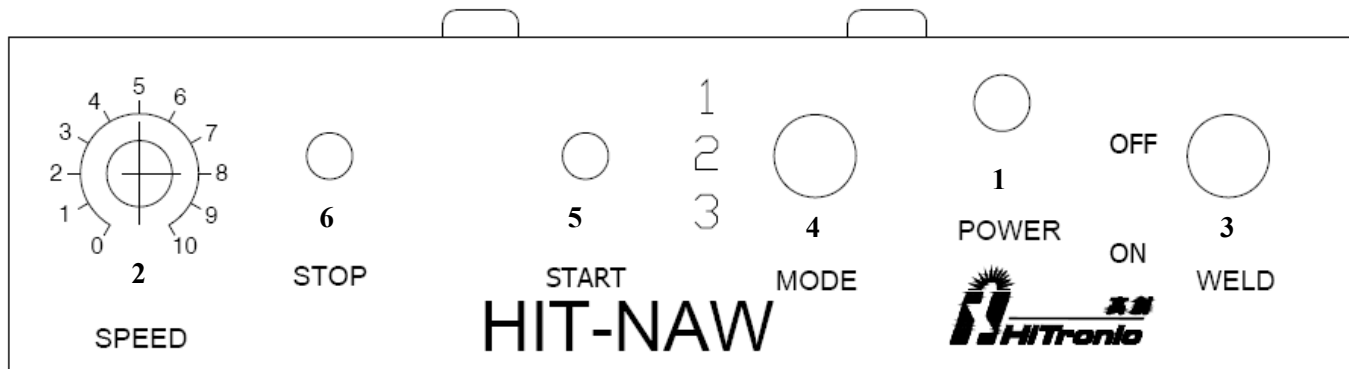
Панель управления сварочной каретки HIT-NAW
